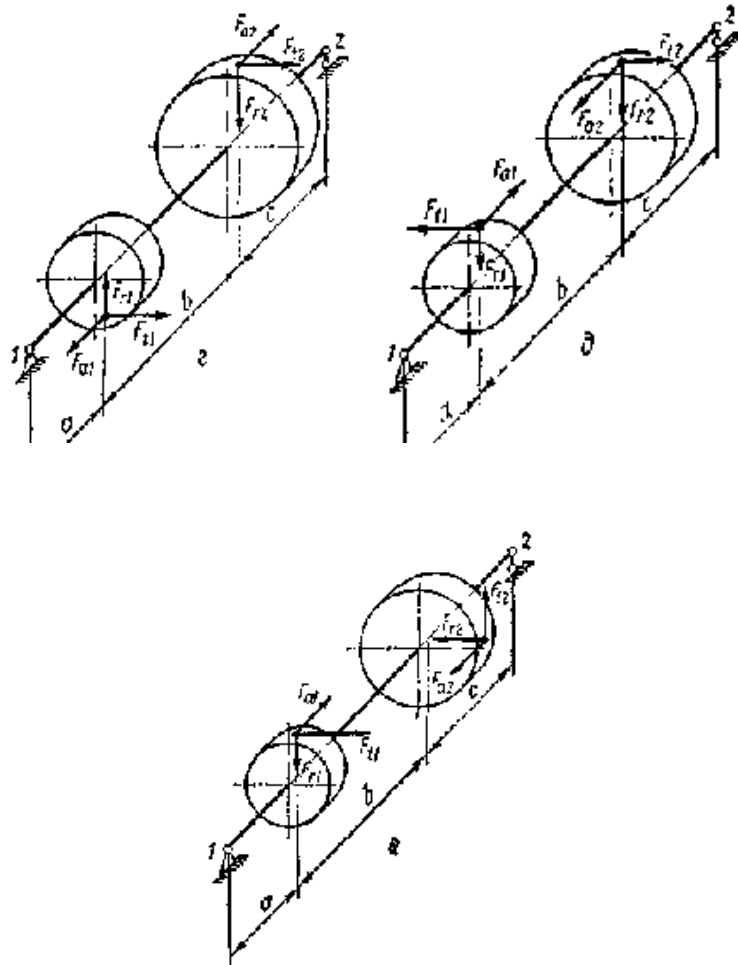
Розрахункові схеми валів багатоступневих передач
